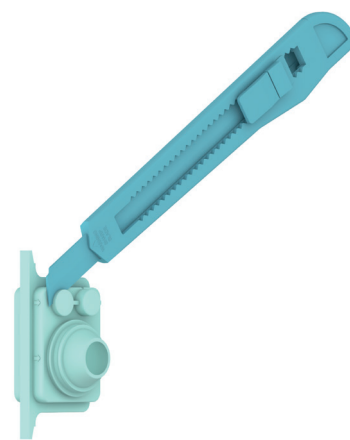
Coupe du bouchon en caoutchouc en entrée de câble
